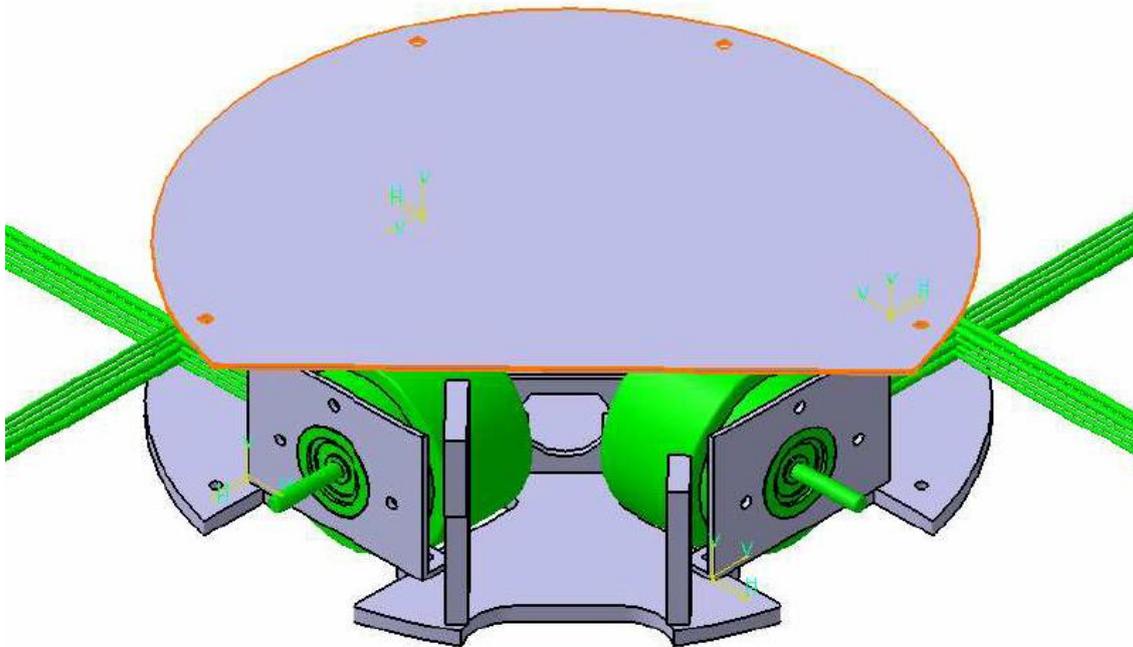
47 Ubicación de la base primera planta en el conjunto robot
